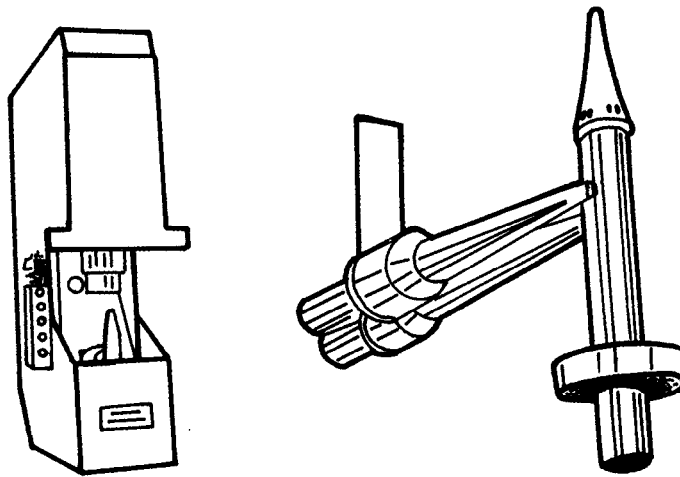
Soldadura ultrasónica de metales.
